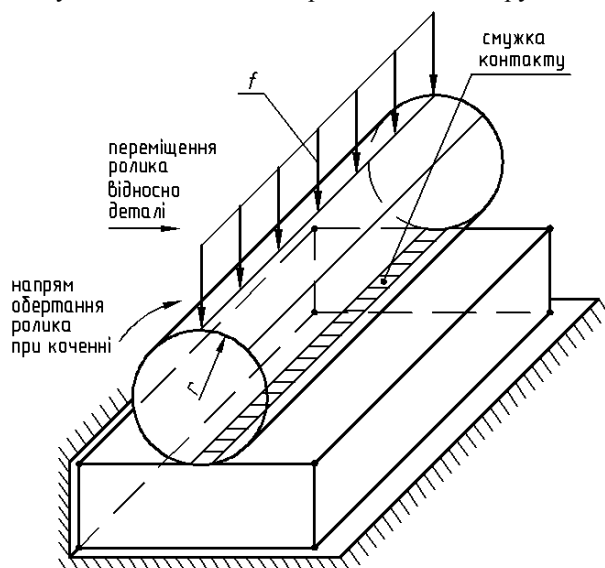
Кочення циліндричного ролика по плоскій деталі
